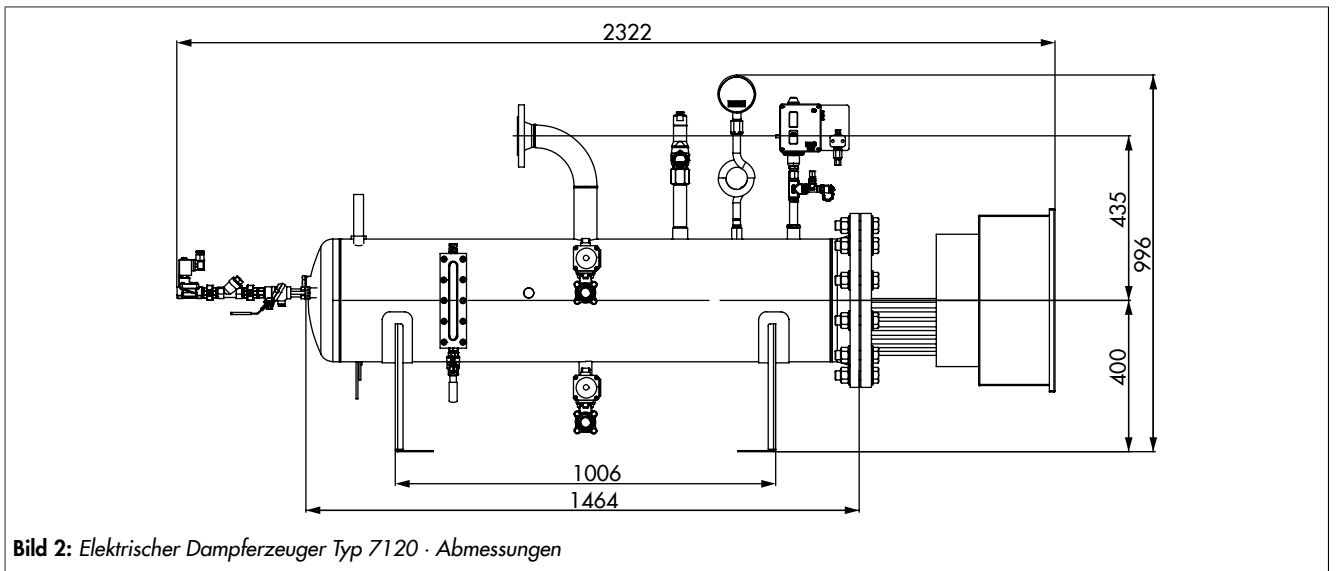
Elektrischer Dampferzeuger Typ 7120 · Abmessungen
